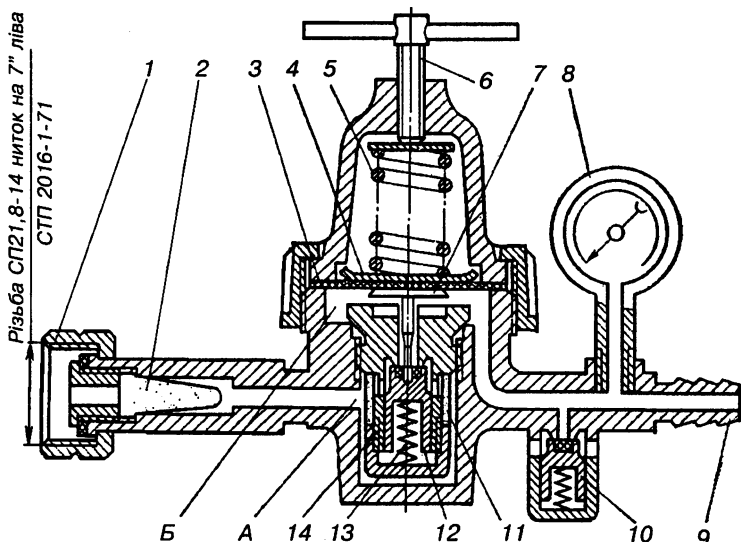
Будова пропан-бутанового редуктора ДПП-1-65:
